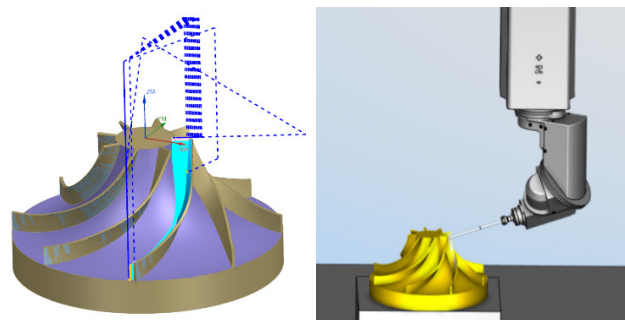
Mô phỏng gia công trên máy CNC 5 trục dạng Head/ Head Rotary Mill
